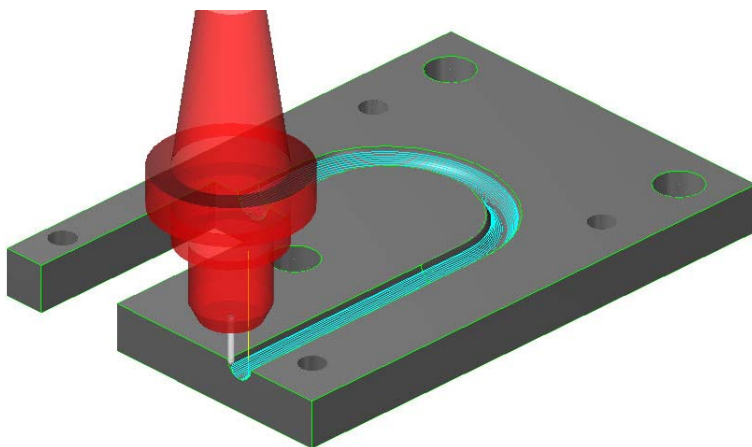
Обработка по потоковым линиям, схема – зигзаг
